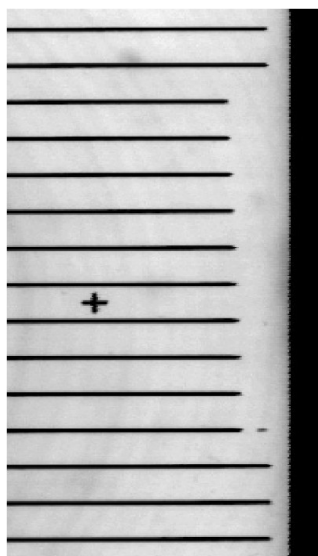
Detail defektu vnitřního pnutí [10]
